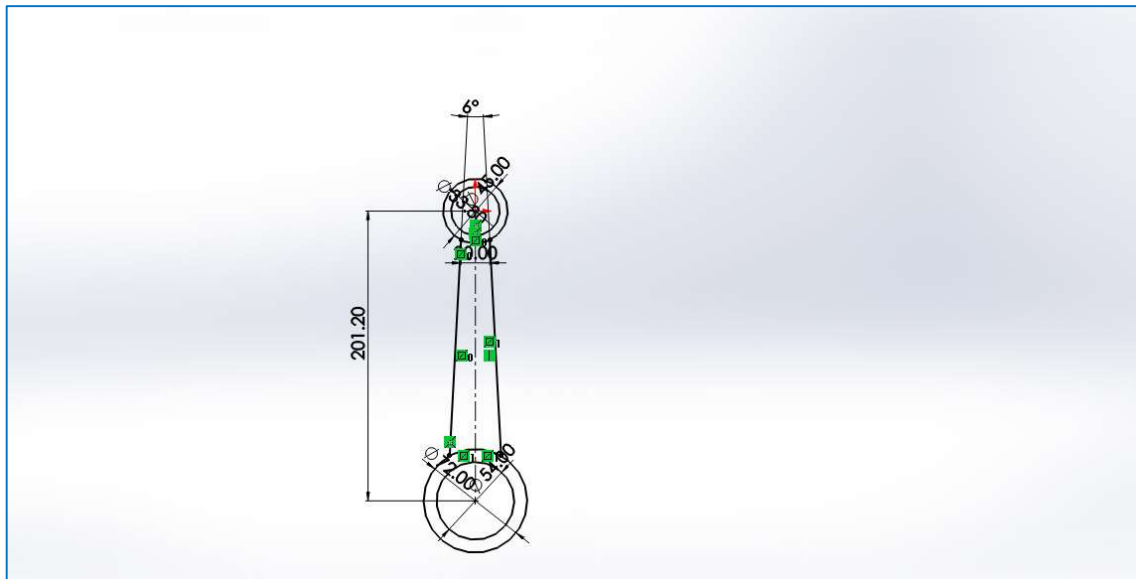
Étape de la construction d'une forme 2D de la bielle
